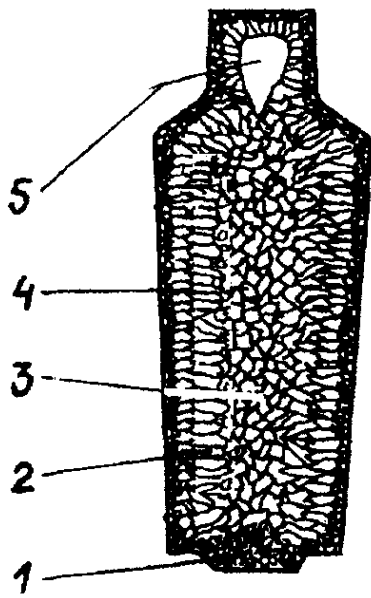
Будова зливка зі спокійної сталі [2]:
